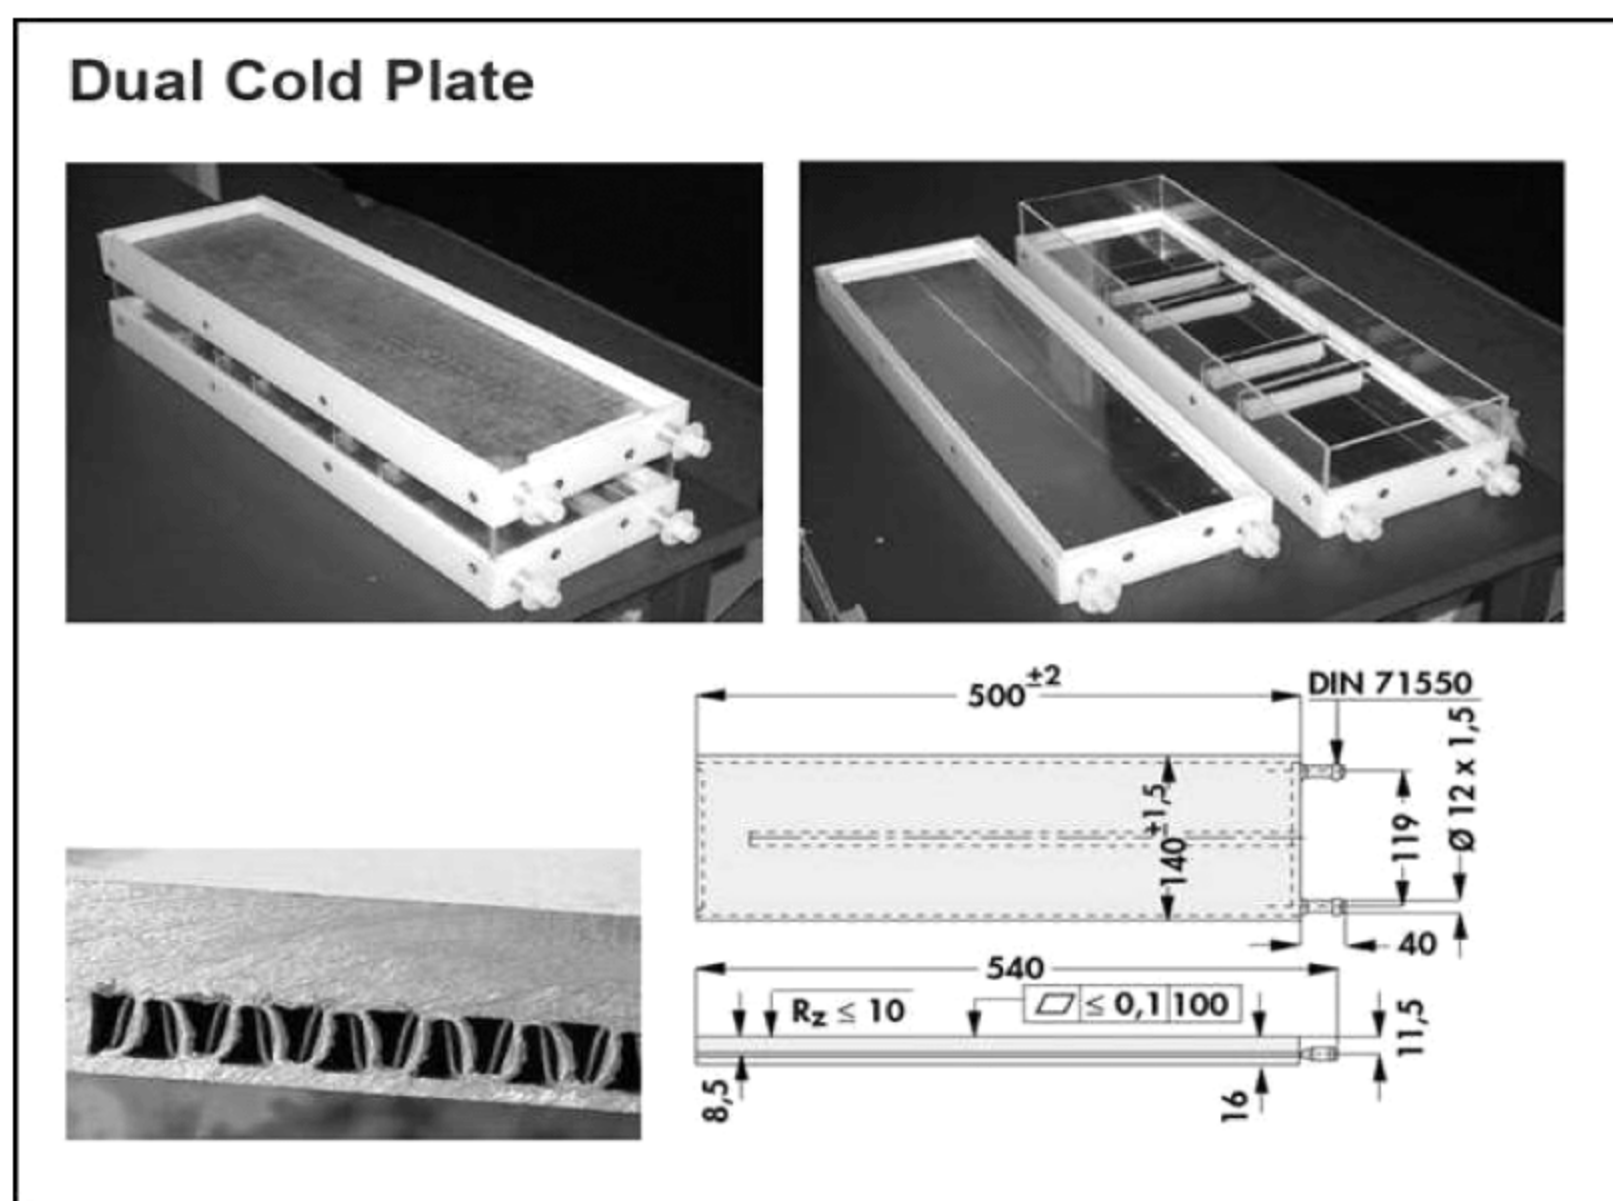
Dual-cold plate 双冷板的外形尺寸以及内部结构
